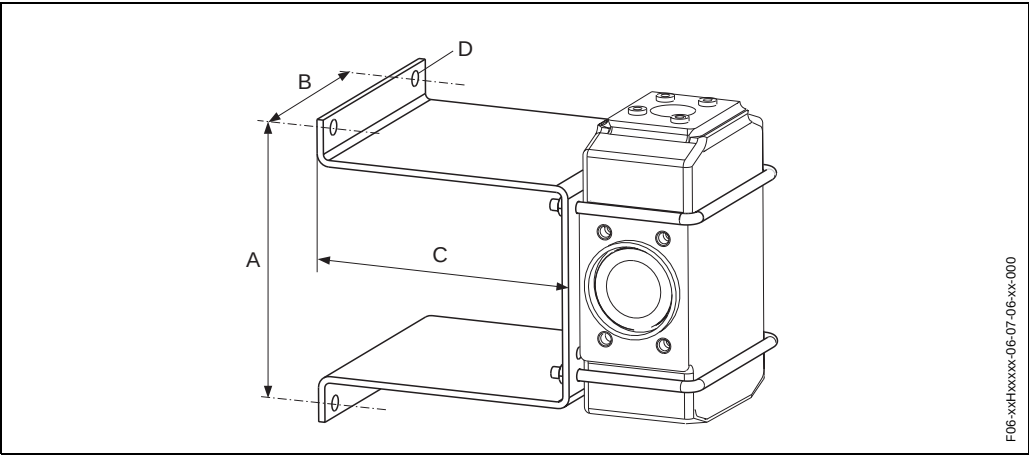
Jogo de montagem de parade para Promag H / DN 2...25
